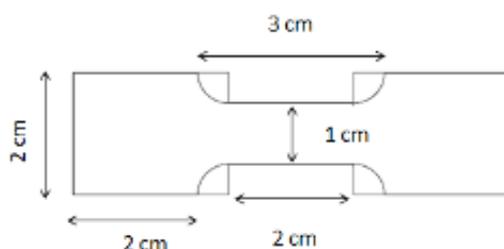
Molde utilizado para os corpos de prova dos filmes para ensaio de tração.
